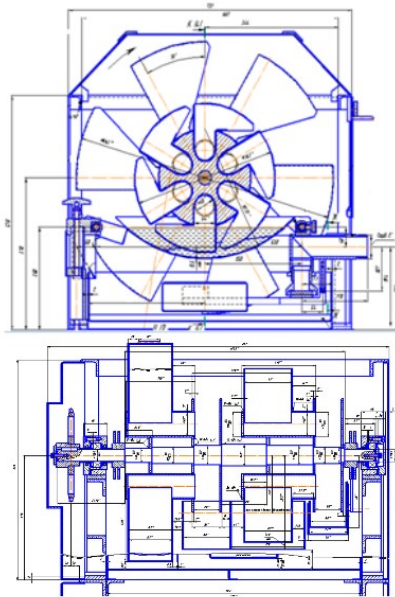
Дозатор черпачкового типа. Габаритный чертеж
